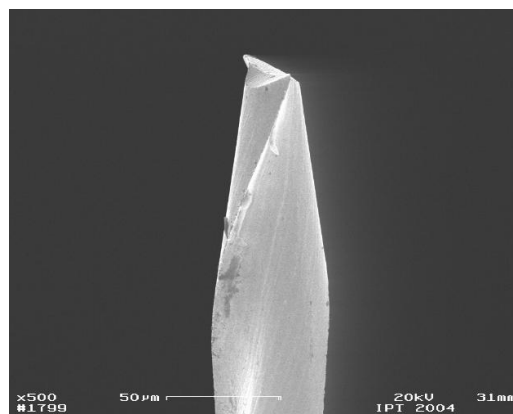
Tvar pro mikrorotor po obrábění.
